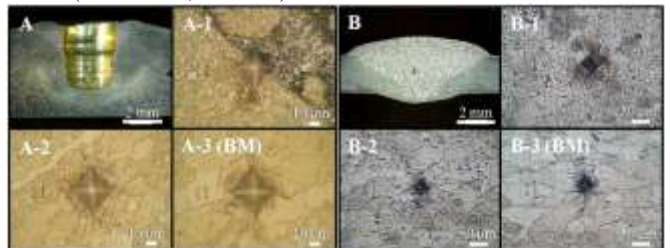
各種接合部断面組織写真 (A: TIG weld, B: FSSW (5.88 kN, 1750 rpm, 6sec))
